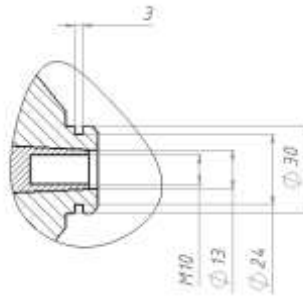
Конструктивные размеры соединения крыльчатки вентилятора с осью электродвигателя
